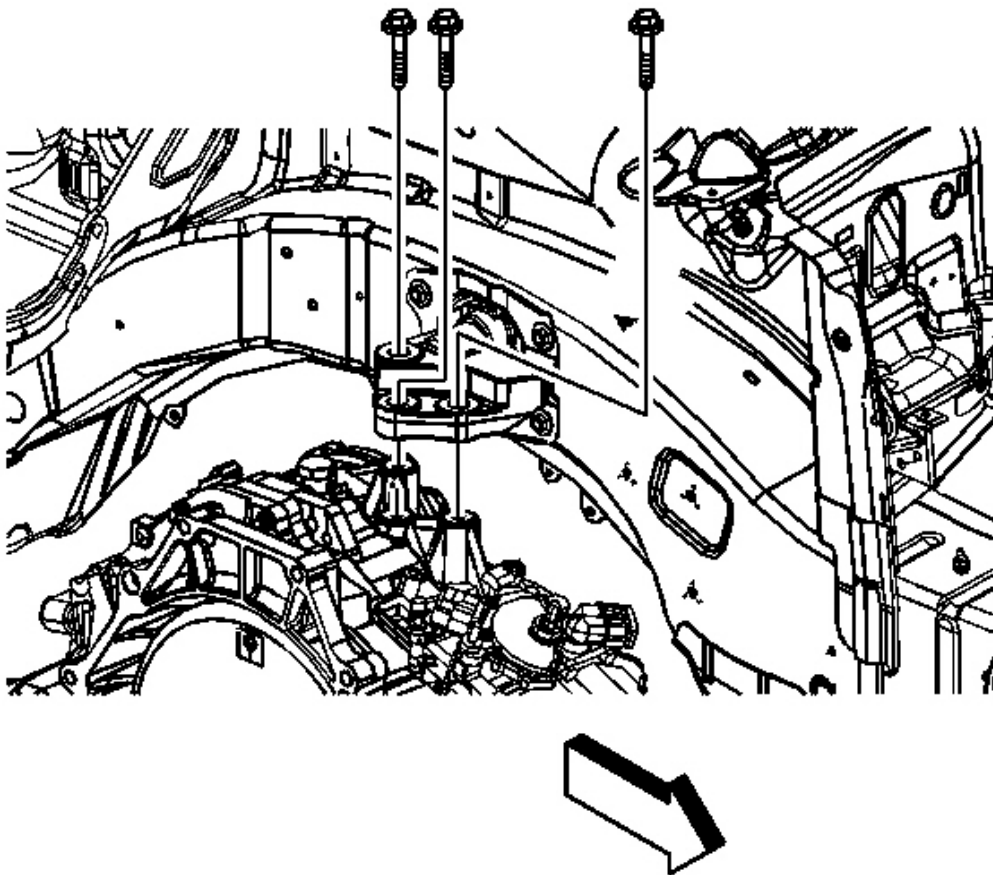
Vista de la derecha Motor Mount & Bolts
